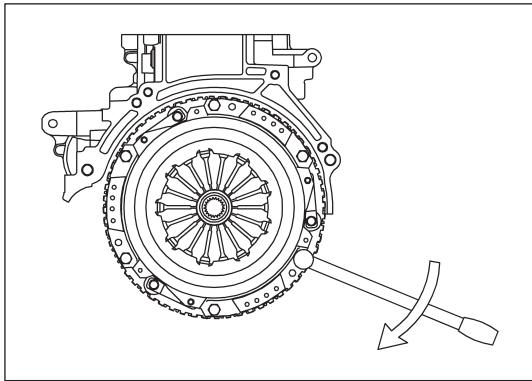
Очередность затягивания кожуха сцепления болтами крепления с пружинными шайбами
